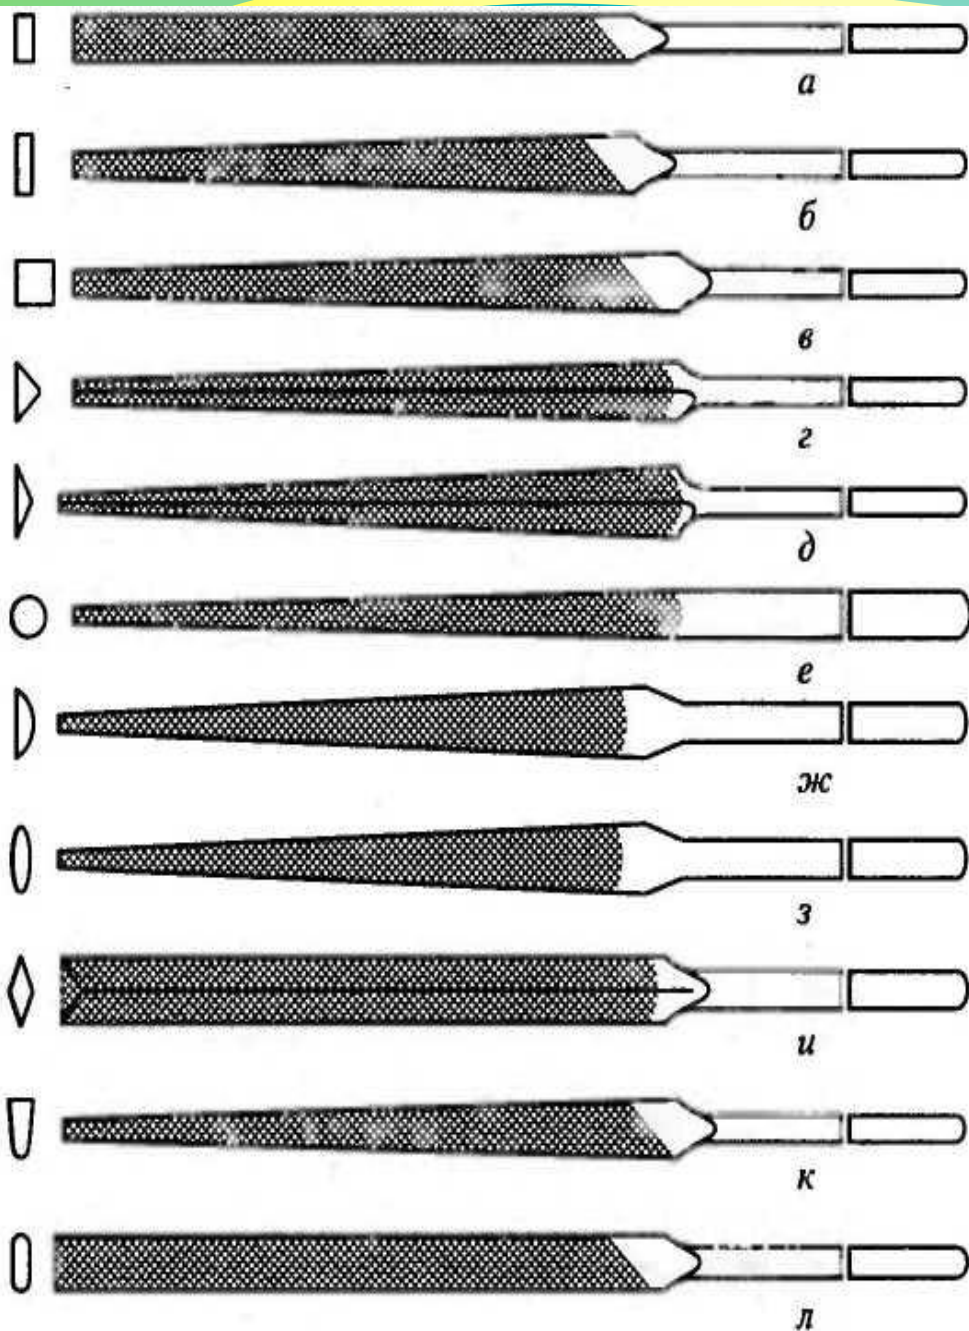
Надфили: а, б - плоские; в — квадратный; г, д — трехгранные; е — круглый; ж — полукруглый; з — оливообразный; и - ромбический; к - трапецеидальный; л - галтельный
